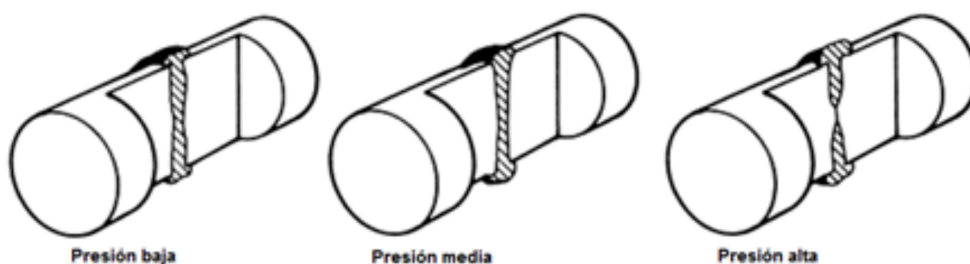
Sección de soldadura por inercia a diferentes presiones axiales. [30]
